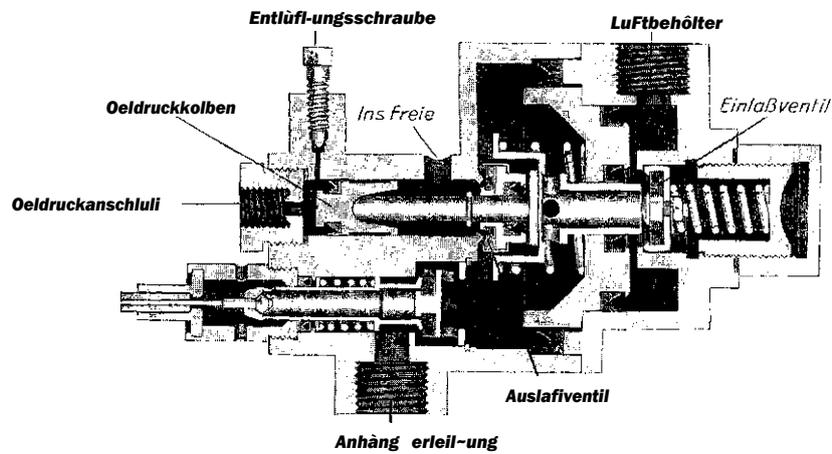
Anhängerbremseventil (Ältere Ausführung mit Seilzug für die Handauslösung)
